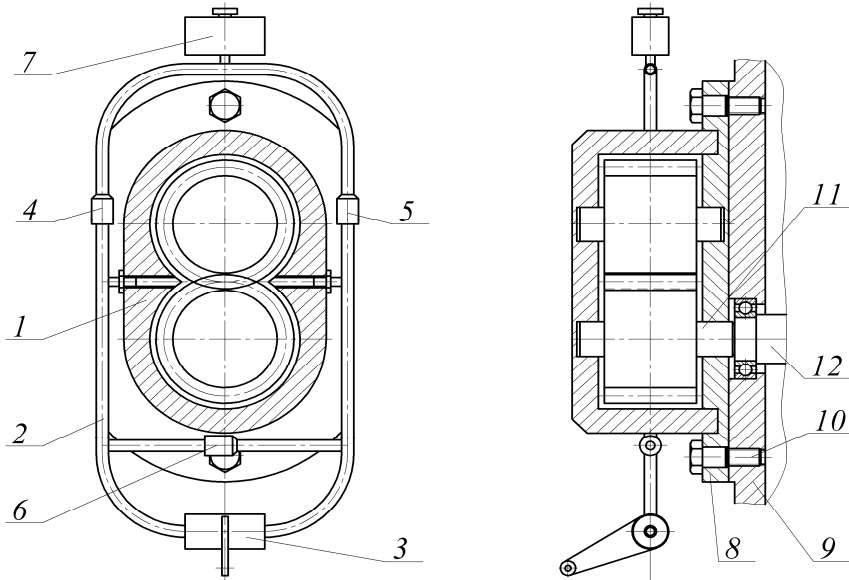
Конструктивна блок - схема установки гальма на редукторі механізму підйому вантажу
